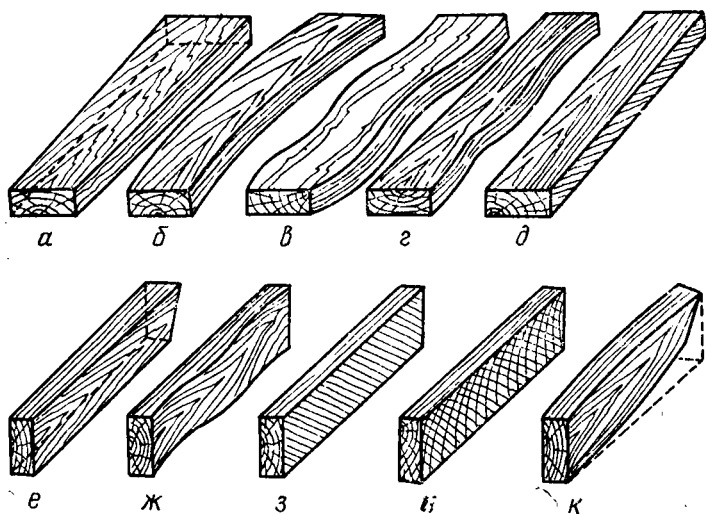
Дефекты распиловки на круглопильных станках:
